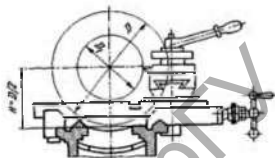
Габариты обрабатываемых на станке заготовок
